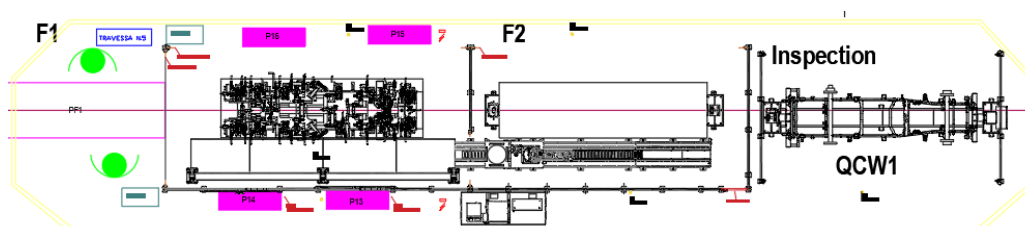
Linha de Soldadura Chassis (Fonte: Toyota Caetano Portugal)
